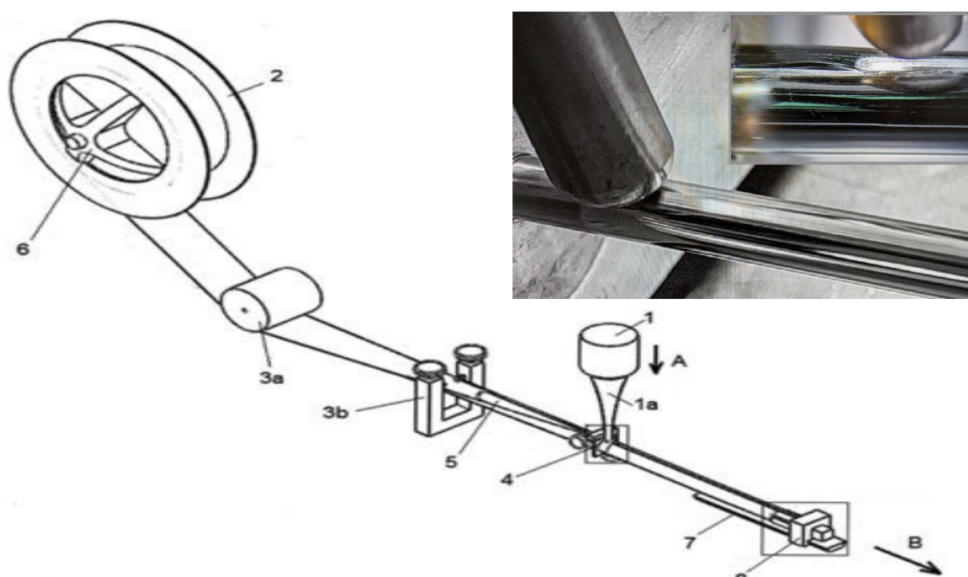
Схема установки ультразвуковой сварки стримерных трубок [6]
